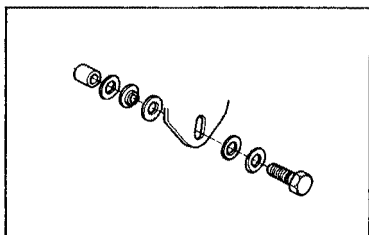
Правильный порядок набора деталей для крепежа ремня безопасности
